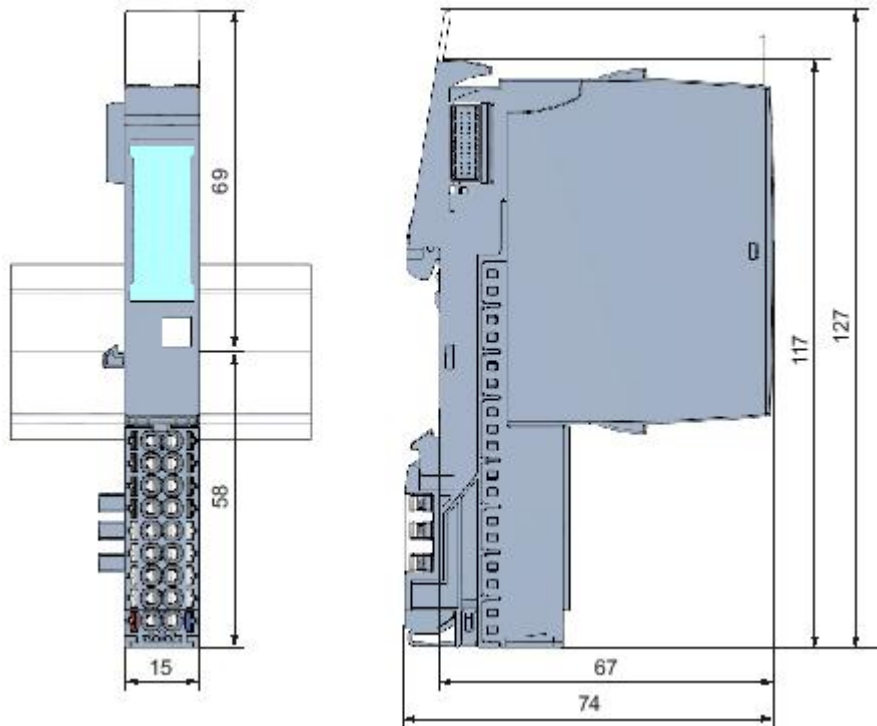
Габаритные размеры BU15-P16+A0+2D
